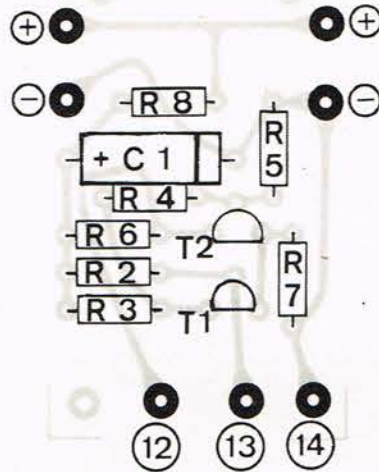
Print til den lysstyrte Schmitt trigger. Komponentplaceringstegning.
